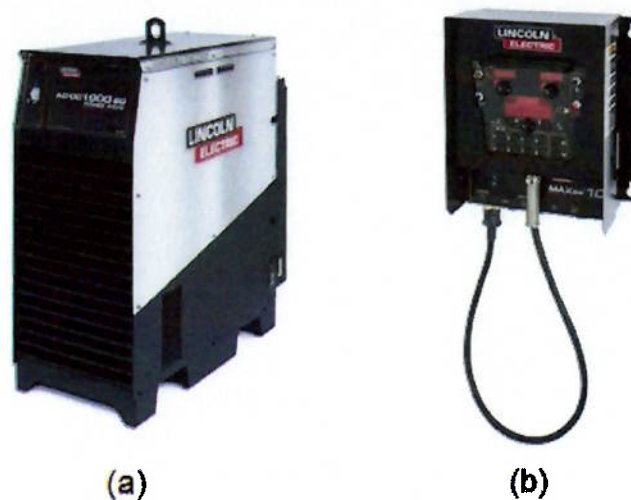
Equipamentos utilizados para a soldagem: (a) fonte de alimentação; (b) controlador.
